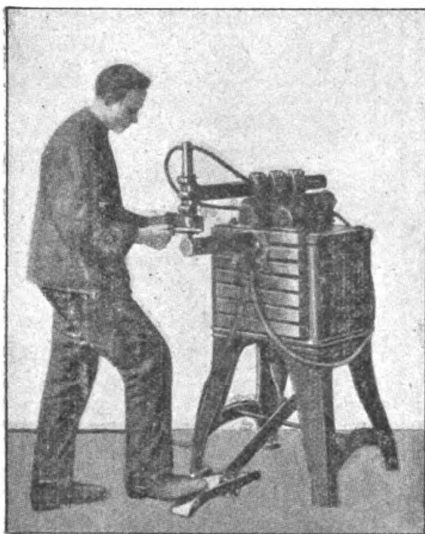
Punktschweißmaschine für Fabrikbetrieb.
